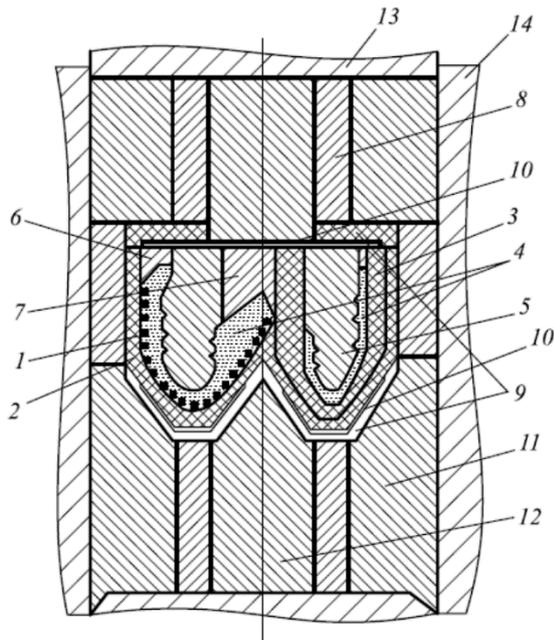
Схема сборки КВД для горячего прессования алмазных долот:
